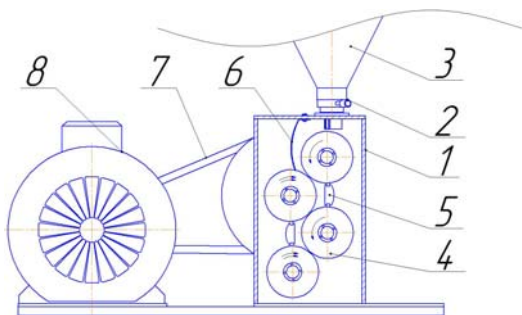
Помельний модуль експериментальної установки для виробництва борошна: 1 – корпус; 2 – дозатор; 3 – живильник; 4 – робочі органи; 5 – підпружинені щітки; 6 – відбивна станка; 7 – клинопасова передача; 8 – асинхронний електродвигун
